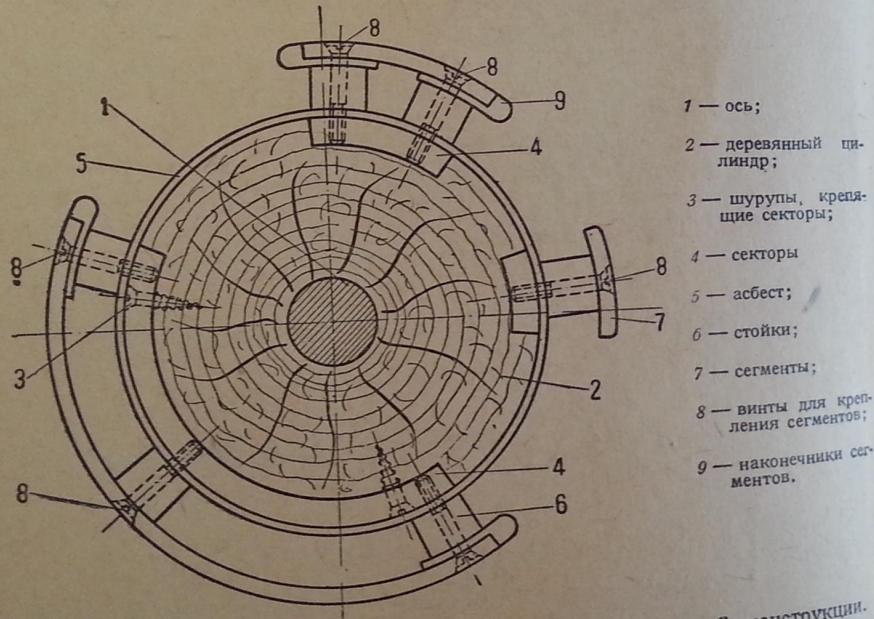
Горизонтальный разрез главного барабана деревянной конструкции.
